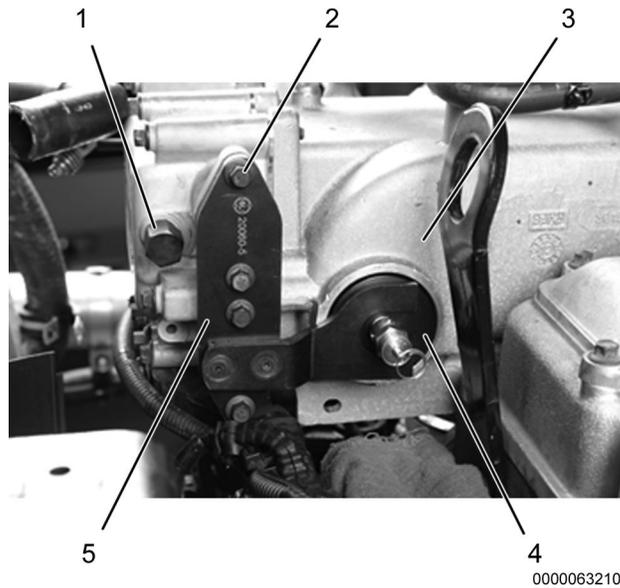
Instalación del tapón del enfriador, disco de tapón grande de chasquido y placa de orificio doble
